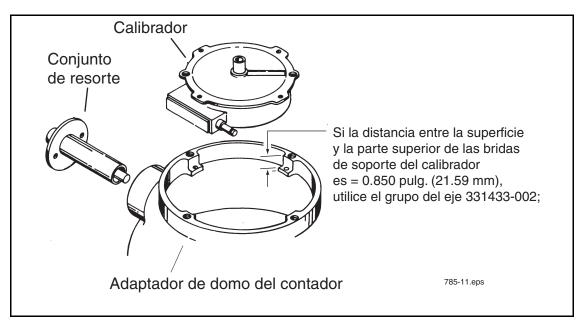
Calibrador, conjunto de resorte y adaptador del domo del contador
